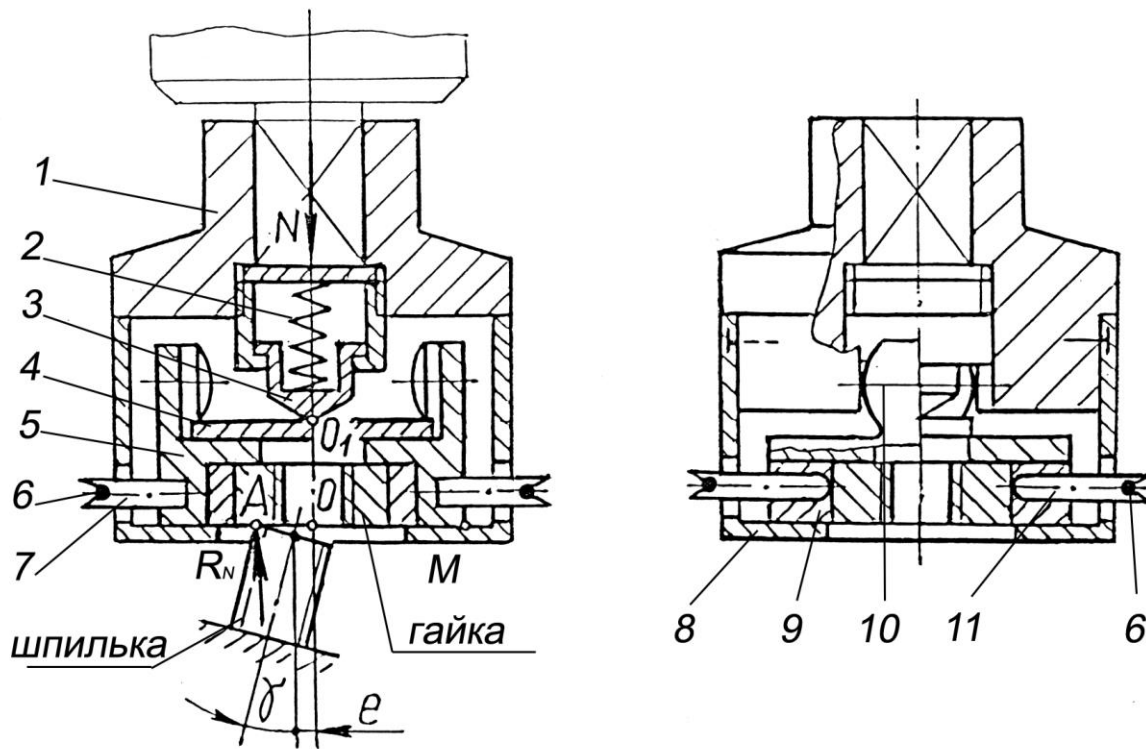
Головка з податливим базуванням гайки: 1- корпус; 2- осьова пружина; 3- втулка; 4- шайба проміжна; 5- напрямна бази гайки; 6 – кільце пружинне; 7, 11 – штифти; 8 – обмежувальна втулка; 9 – база гайки; 10 – заокруглені виступи напрямної 5.
